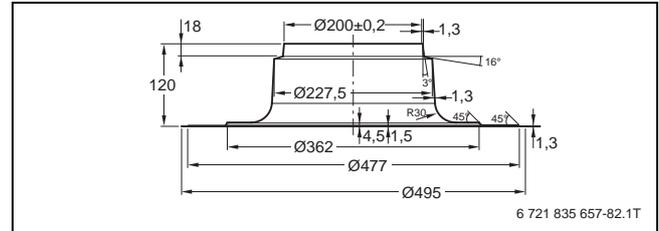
Flachdach-Klebeflansch (Maße in mm)
